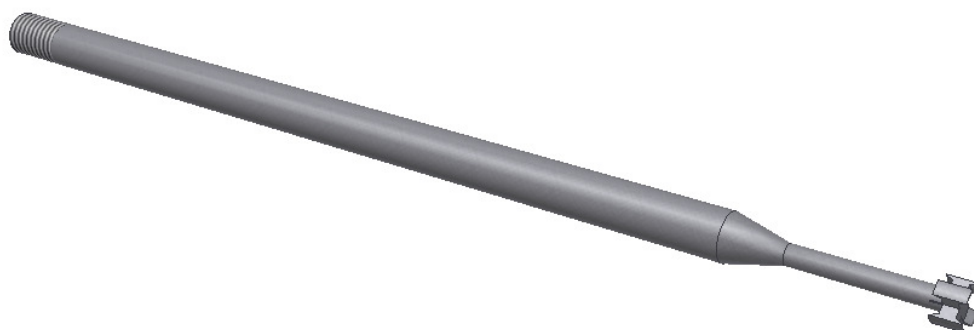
Skica odpeckovače s pákou pro upnutí přísátím
